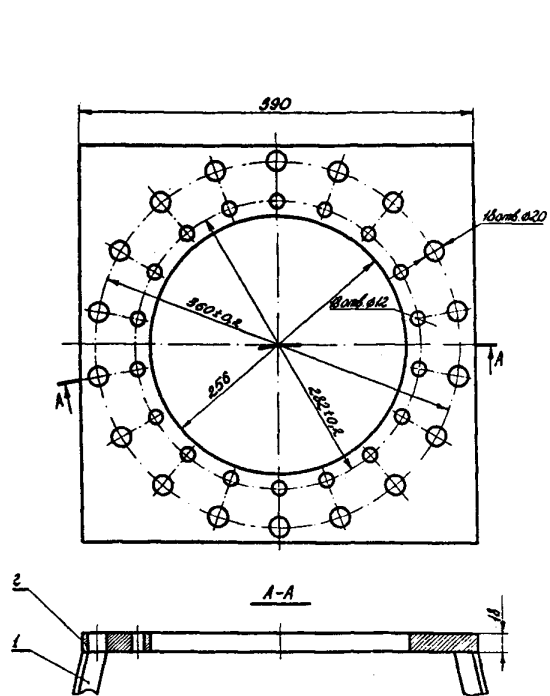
Подставка для разборки и сборки газительной камеры и отделителя:
